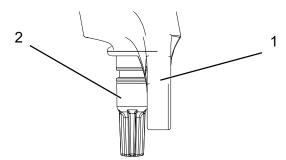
Suntour-Zugstufen-Schraube (2), Gabel (1)
